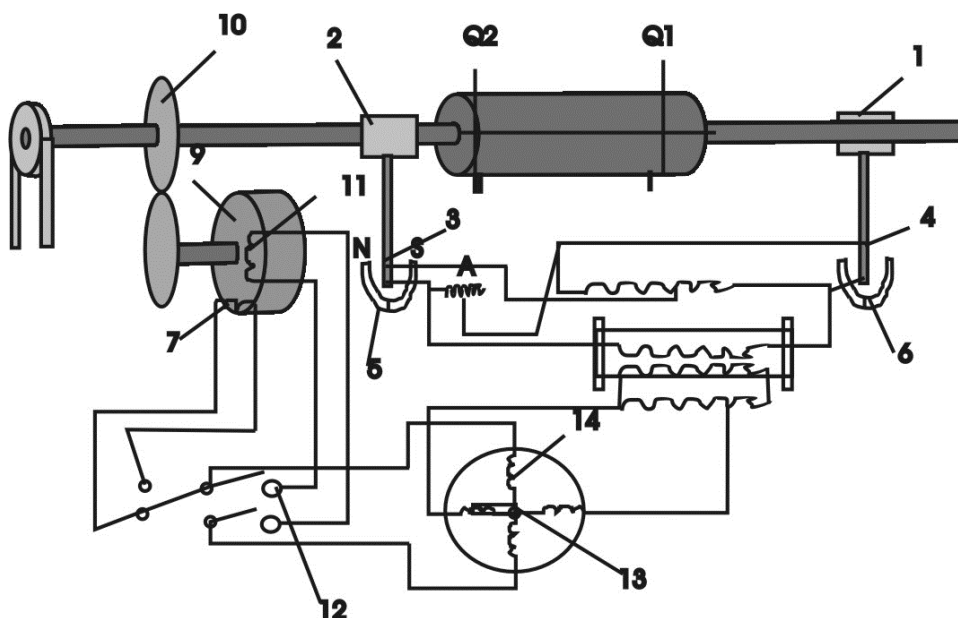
Схема балансировочного станка с качающимися опорами и с электрическими связями:
